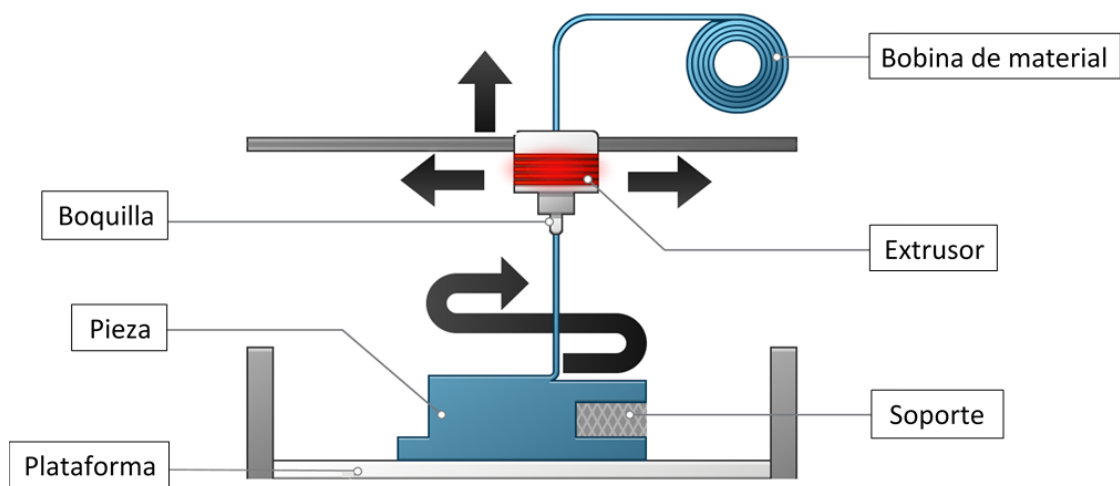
b Esquema de máquina de modelado por deposición fundida.
